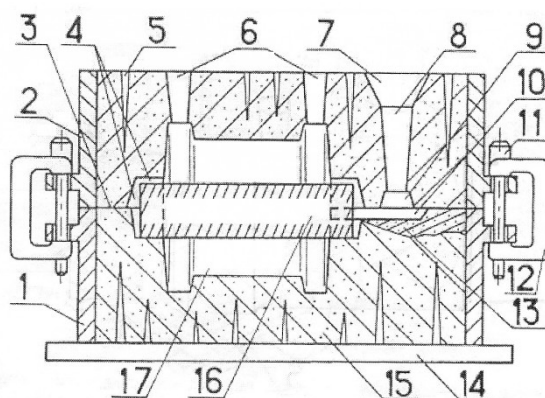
Эскиз песчаной литейной формы в сборе: 1 – нижняя опока; 2 – верхняя опока; 3 – плоскость разъема; 4 – зазоры; 5 – вентиляционный канал; 6 – выпоры; 7 – литниковая чаша; 8 – стояк; 9 – шлакоуловитель; 10 – питатель; 11 – центрирующий штырь; 12 – скоба; 13 – местный разрез; 14 – плита; 15 – формовочная смесь; 16 – стержень; 17 – рабочая полость формы
